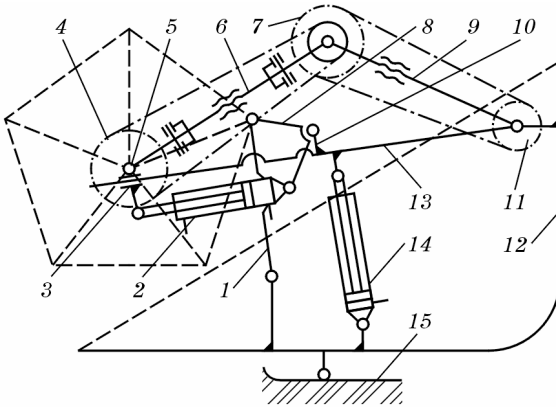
Схема заблокованого механізму регулювання положення мотовила:
